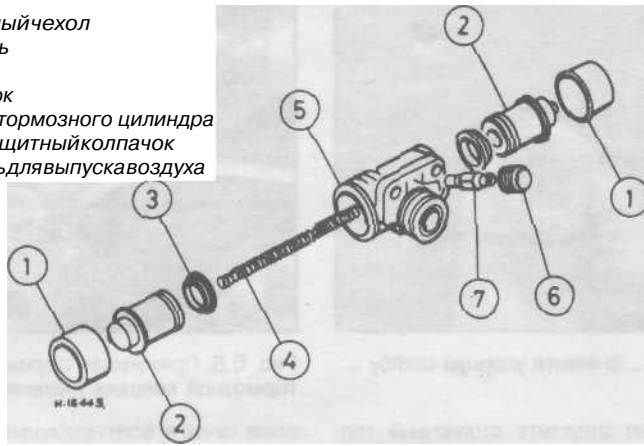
Детали заднего колесного цилиндра (типичные)
